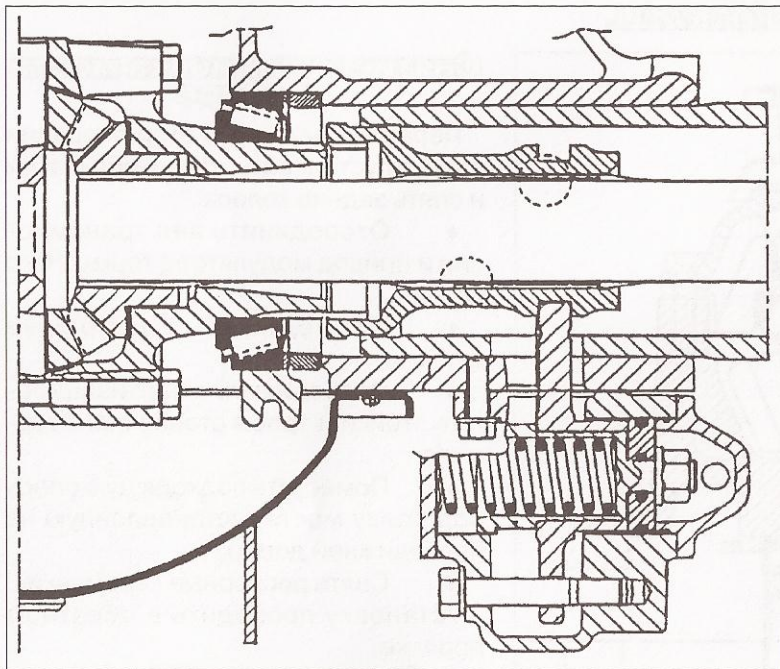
Разрез привода механизма блокировки дифференциала.
